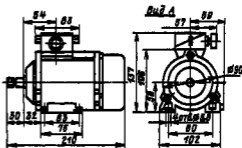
16 Габаритные и установочные размеры двигателей АА50А2Н и АА50А16Н
